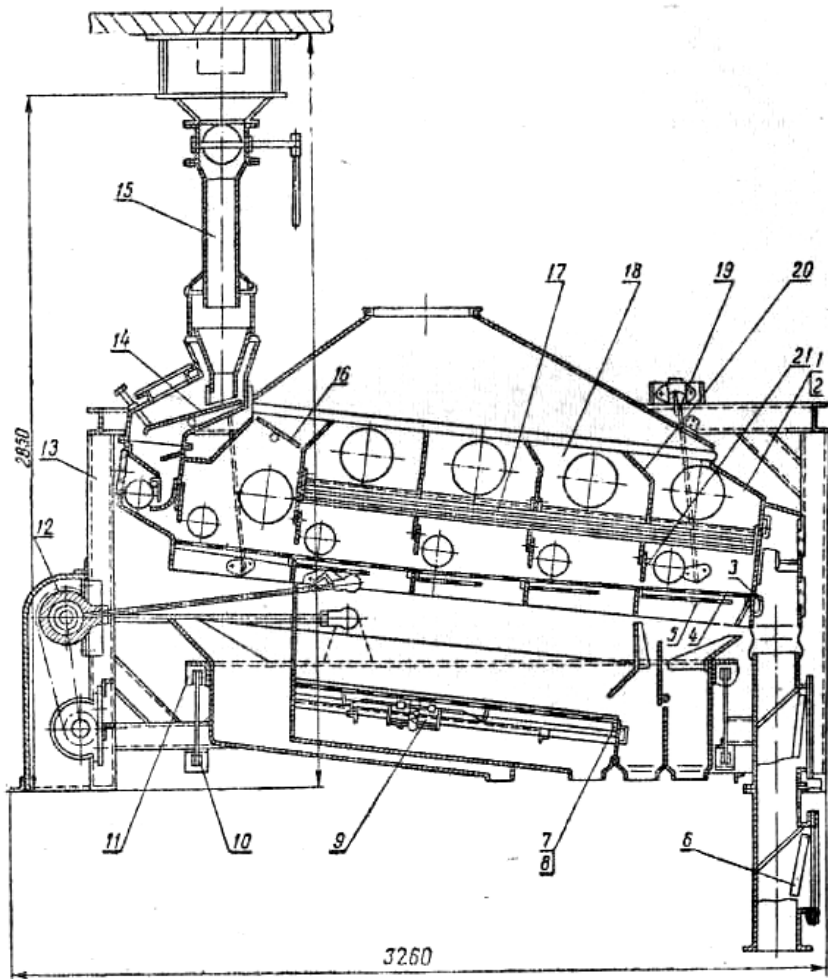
Зерноситовійочна машина А1-БЗГ: 1, 2 - правий і лівий ситові кузови; 3 - ситова рама; 4 - решітка; 5 - піддон ситової рами; 6 - еластичний клапан; 7, 8 - їхні обойми кузова-збірки; 9 - інерційний механізм для очищення сит; 10 - пружинна стійка; 11 - кузов-збірник; 12 - ексцентриковий коливальник; 13 - станина; 14 - віброрітковий живильник; 15 - приймальний пристрій; 16 - клапан; 17 - жолобкова рама; 18 - аспіраційний збірник; 19 - плоска пружина; 20 - перегородка; 21 - шибер
